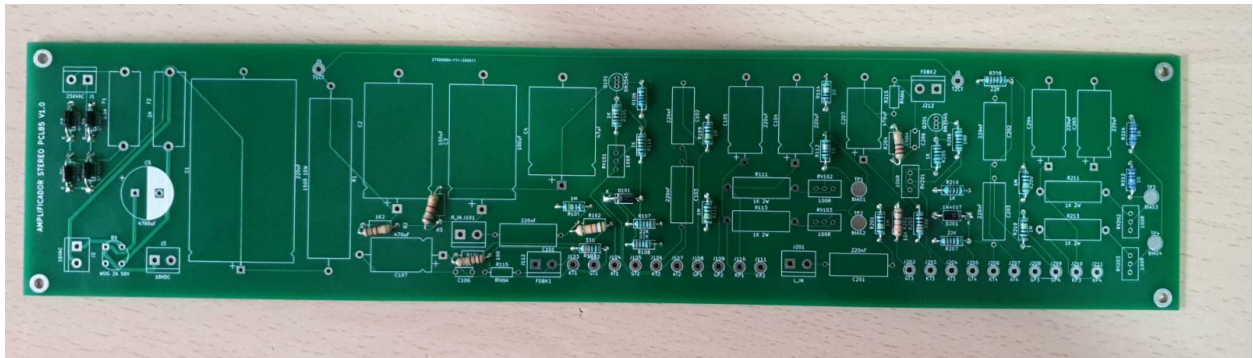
Componentes de menor tamaño soldados al PCB.
